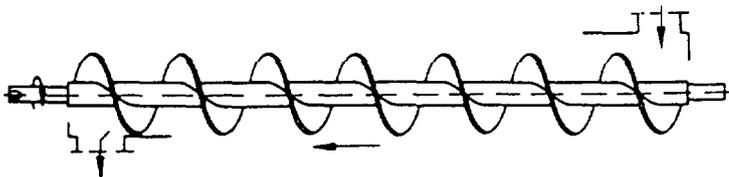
Vollschnecke (Förderschnecke mit Welle) [11]
